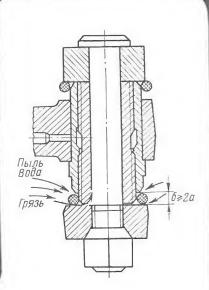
Разрез узла резьбового шарнира: 1 — головки рычагов передней подвески: 2 — наружная резьбовая втулка; 3 — распорная резьбовая втулка; 4 — головка стойки; 5 — защитиое резиновое кольцо; 6 — специальная гайка; 7 — резьбовой палец; 8 — масляный канал; 9 — игольчатый подшипник; а и б — контрольные размеры.
